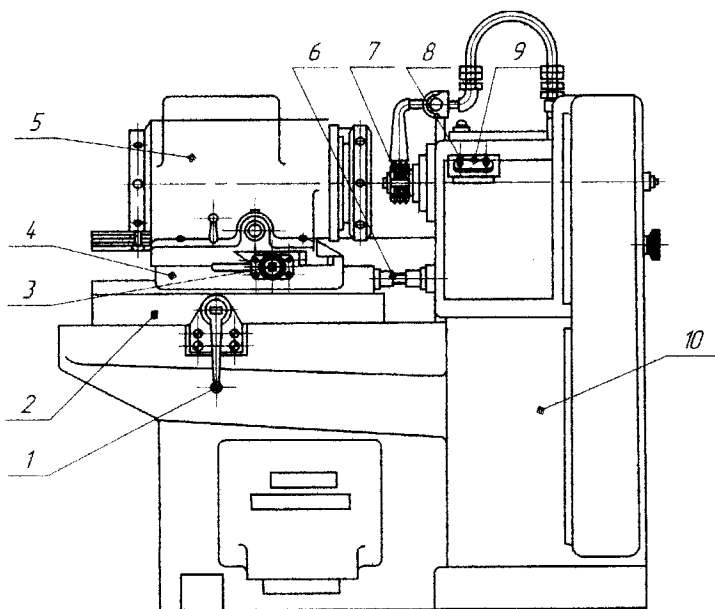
Загальний вигляд різьбофрезерного верстата моделі 563В: 1 – рукоятка повздовжнього переміщення каретки; 2 – каретка; 3 – гвинт поперечного переміщення бабки виробу; 4 – поперечні салазки; 5 – бабка виробу; 6 – регульований упор для точного підведення бабки в робоче положення; 7 – фреза; 8 – фрезерна головка; 9 – кнопкова станція; 10 – стіна
